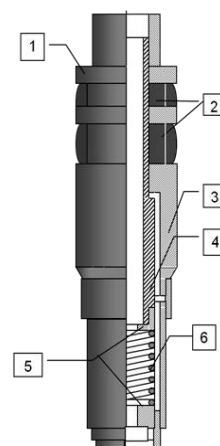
Пакер с упором на забой: 1 - упорное кольцо; 2 - уплотнительная манжета; 3 - корпус пакера; 4 - ствол пакера; 5 - регулировочные шайбы; 6 - демпфирующая пружина
